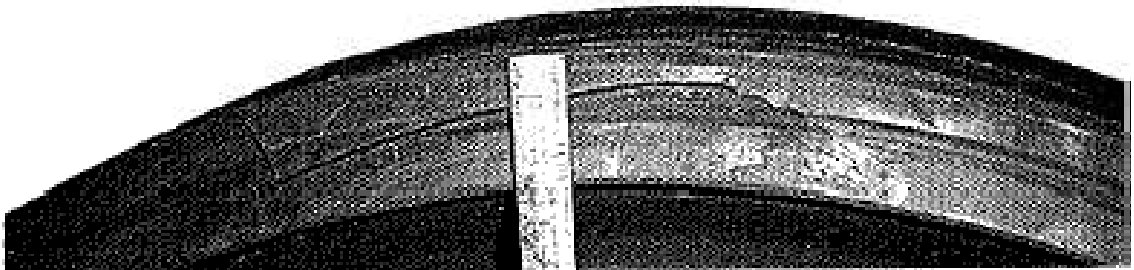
Fisura por fatiga subsuperficial que se ha propagado sobre la cara de la llanta
